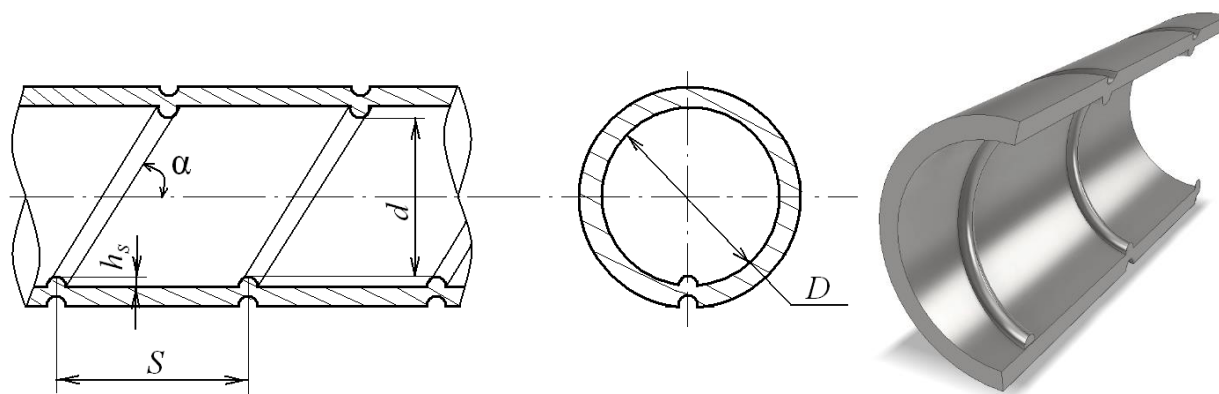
Общий вид трубы с винтовой накаткой
